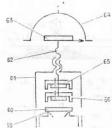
Схема предохранительного клапана: 59 — седло; 60 — выпускной клапан; 61 — крышка; 62 — ходовой винт; 63 — ручка; 64 — шквал; 65, 66 — грузы
